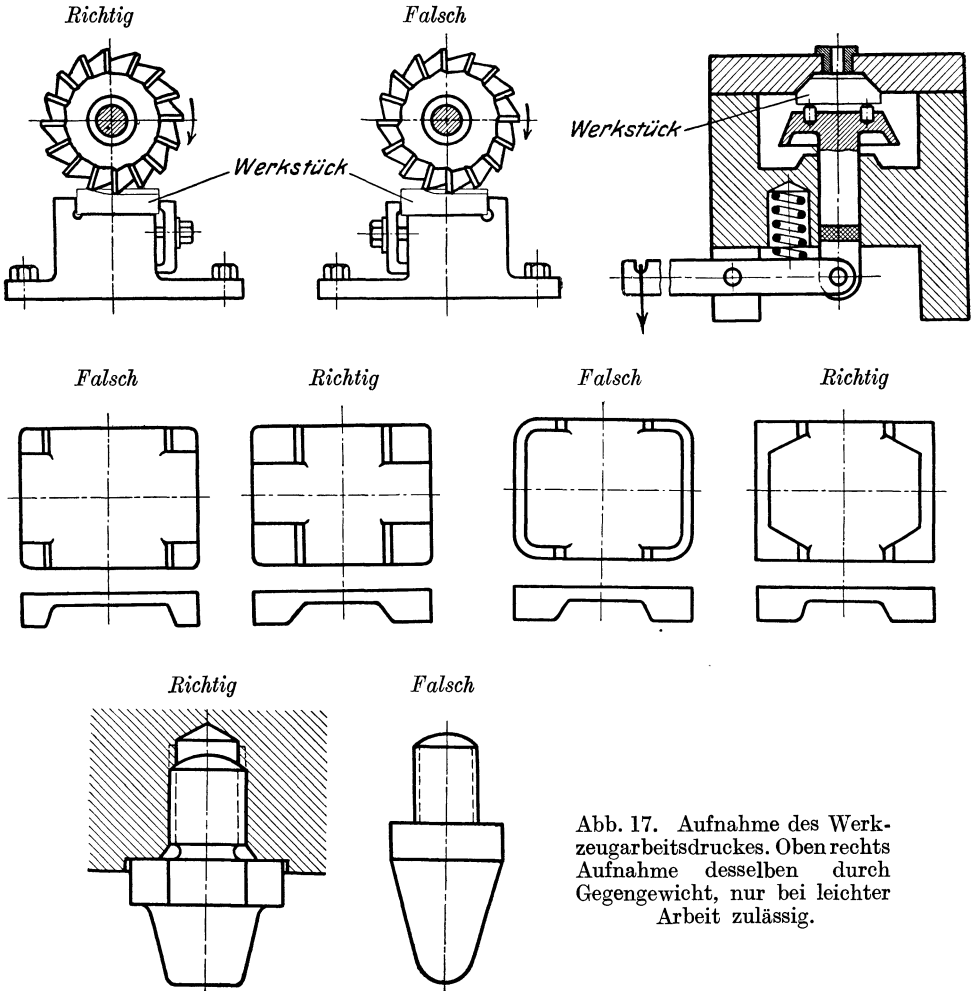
Aufnahme des Werkzeugarbeitsdruckes. Oben rechts Aufnahme desselben durch Gegengewicht, nur bei leichter Arbeit zulässig.
